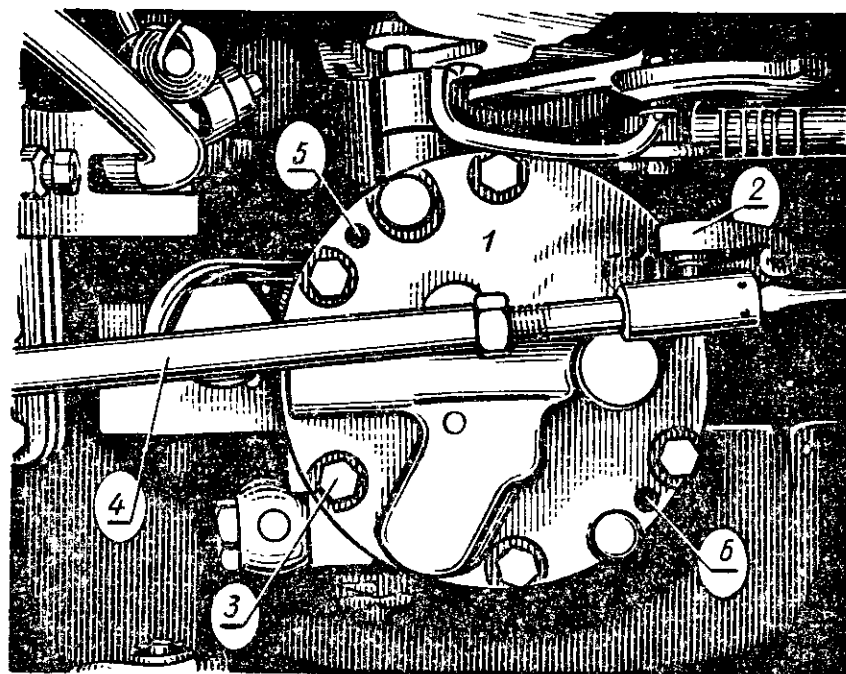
Вывертывание пробки из наконечника тяги педали слива: 1 — крышка фильтра коробки передач; 2 — рычаг педали слива; 3 — болт; 4 — тяга педали слива; 5 и 6 — резьбовые отверстия под демонтажные болты.
